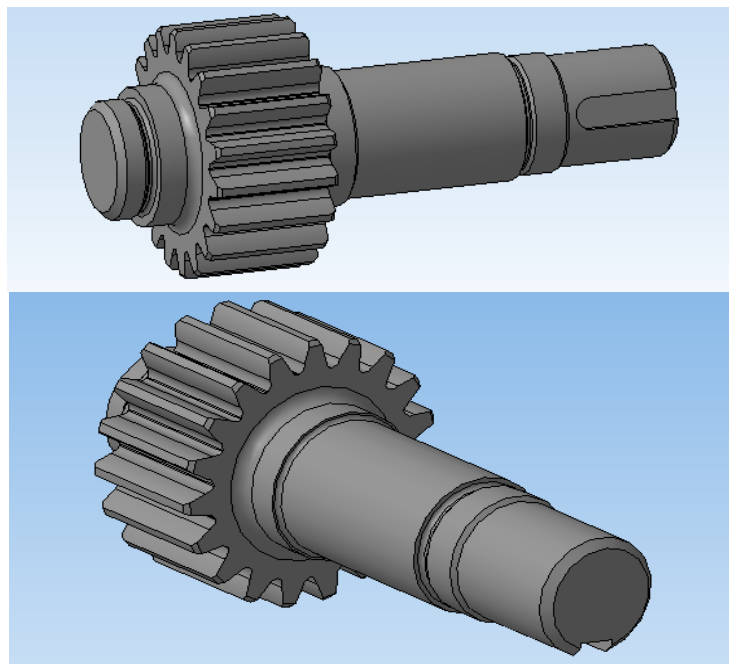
3–D модель деталі «Вал-шестерня»
